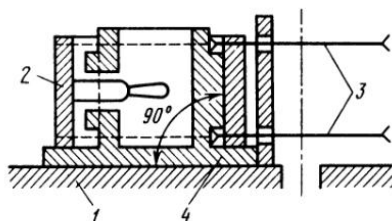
Опилка ящика на фрезерном станке по шаблону:
